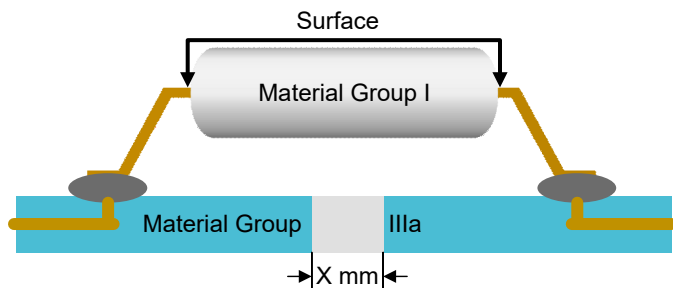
通过槽切口来增加 PCB 爬电距离的 PCB 横截面积。
